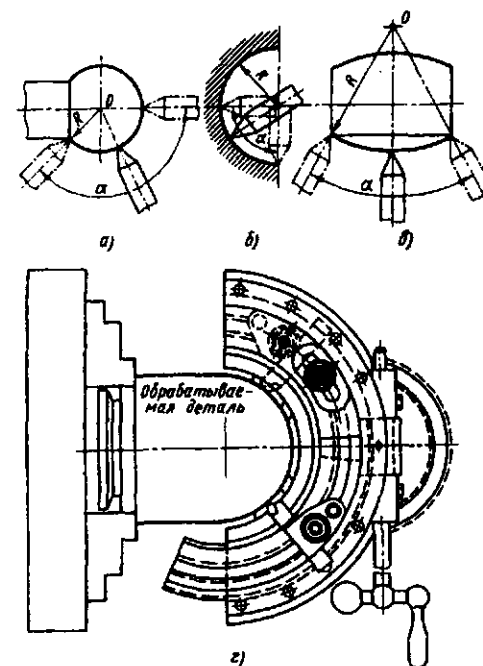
Схемы обработки фасонных поверхностей заготовок
